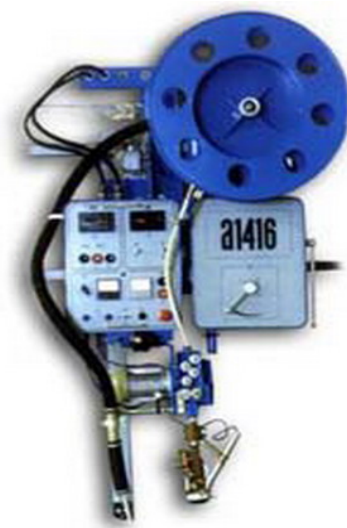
Автомат для дуговой сварки А-1416
